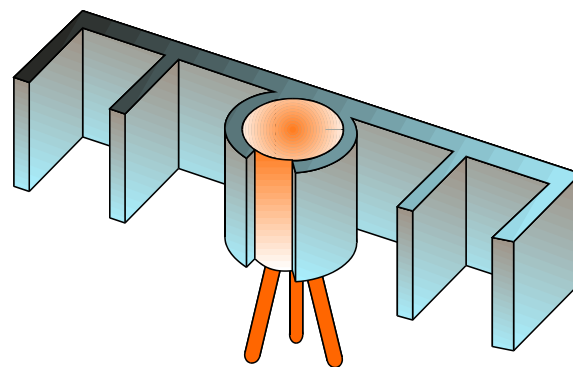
Transistor de corpo cilíndrico com dissipador de calor.
